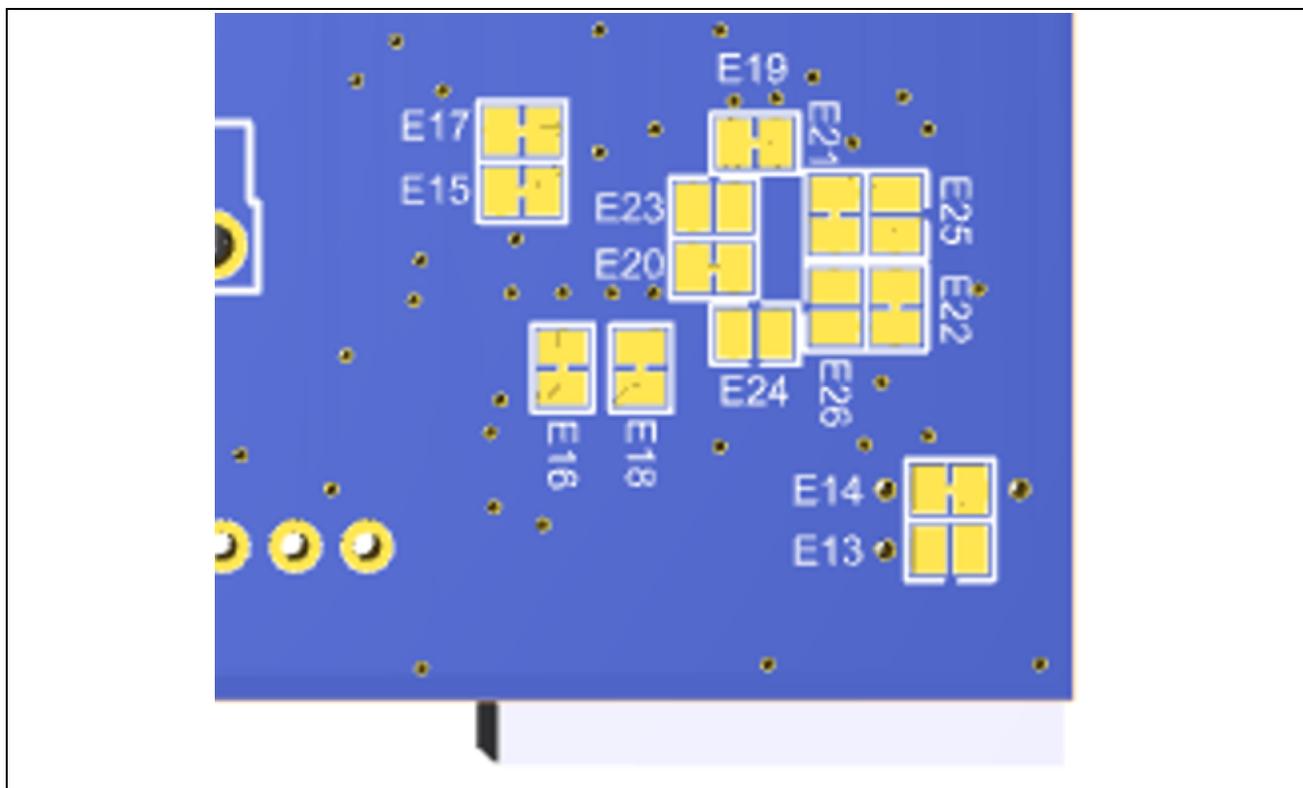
Pmod 2 Jumper Trace Cut / Solder Bridge 配置 (はんだ面)
